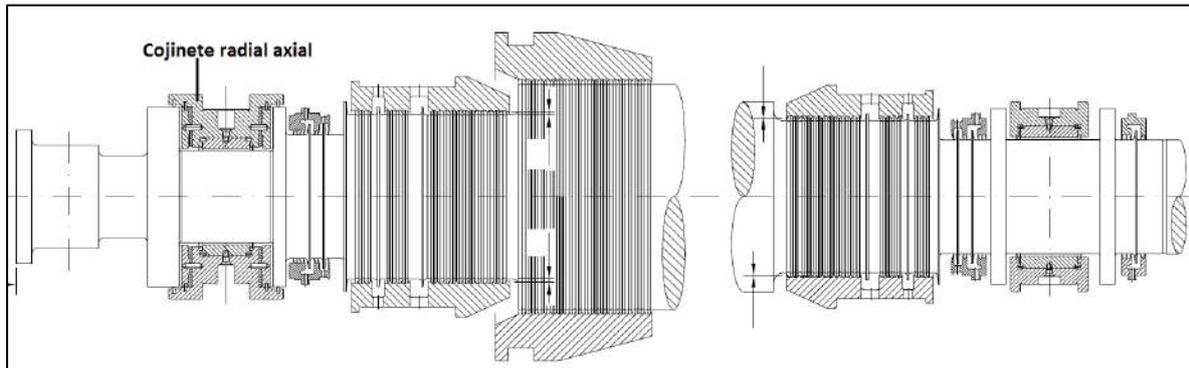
Vista general del rotor de la turbina donde se especifica la posición del cojinete radial-axial.
